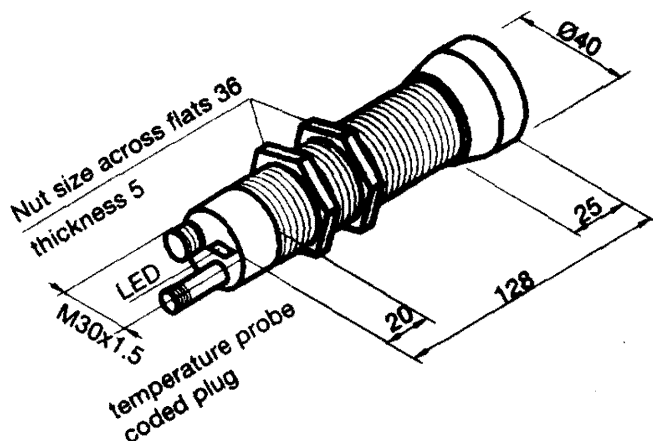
Внешний вид и габаритные размеры датчика уровня Honeywell
